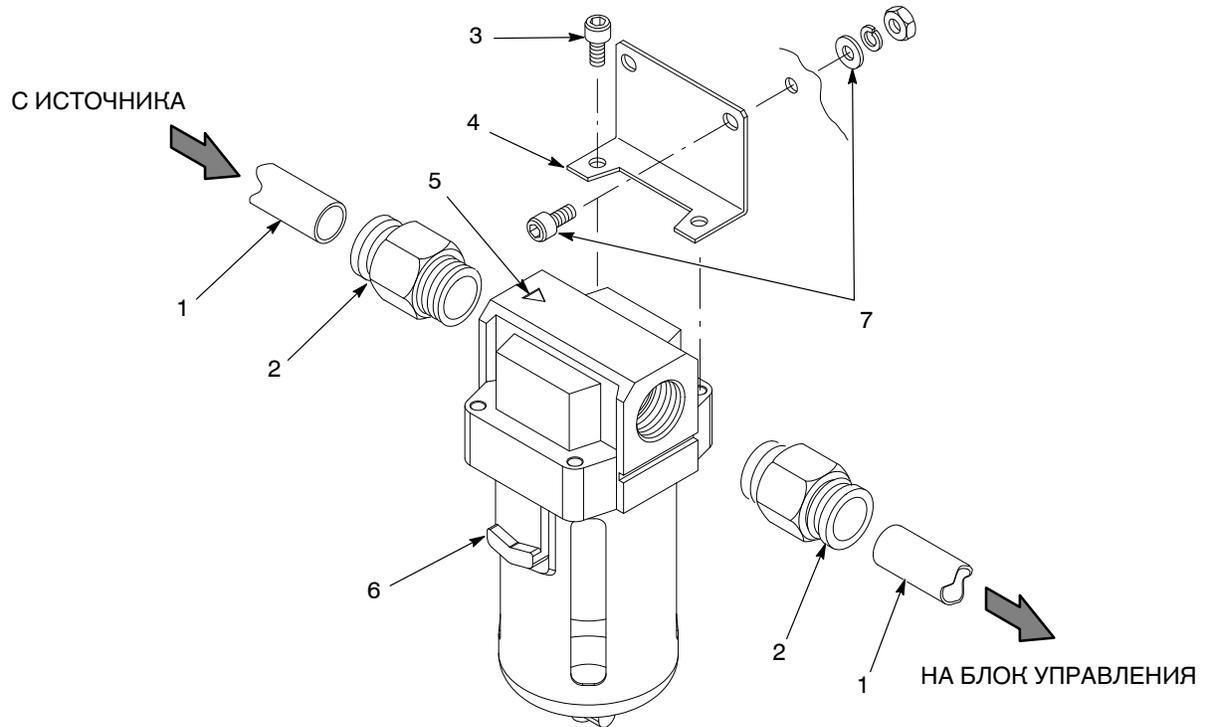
Монтаж воздушного фильтра – системы для монтажа на стене и на ручне
